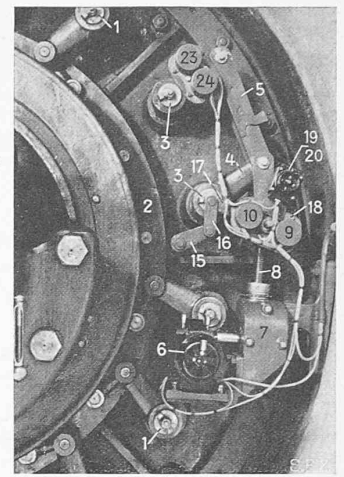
Ansicht der Turbinen-Reinigungsvorrichtung nach Patent Dietrich
